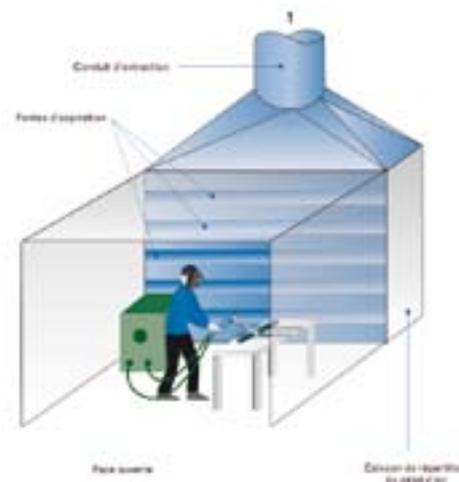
CABINE DE SOUDAGE (SOURCE INRS)
